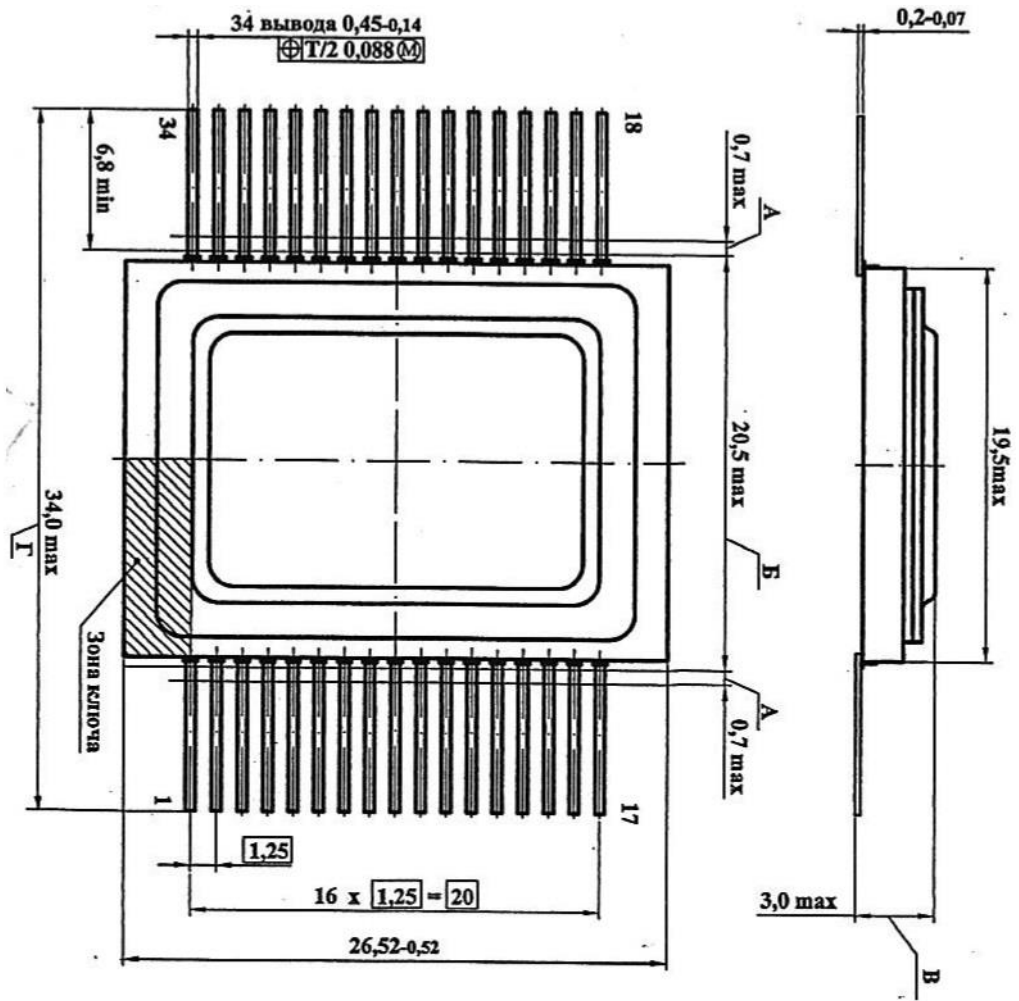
Габаритный чертеж корпуса 4137.34-3
